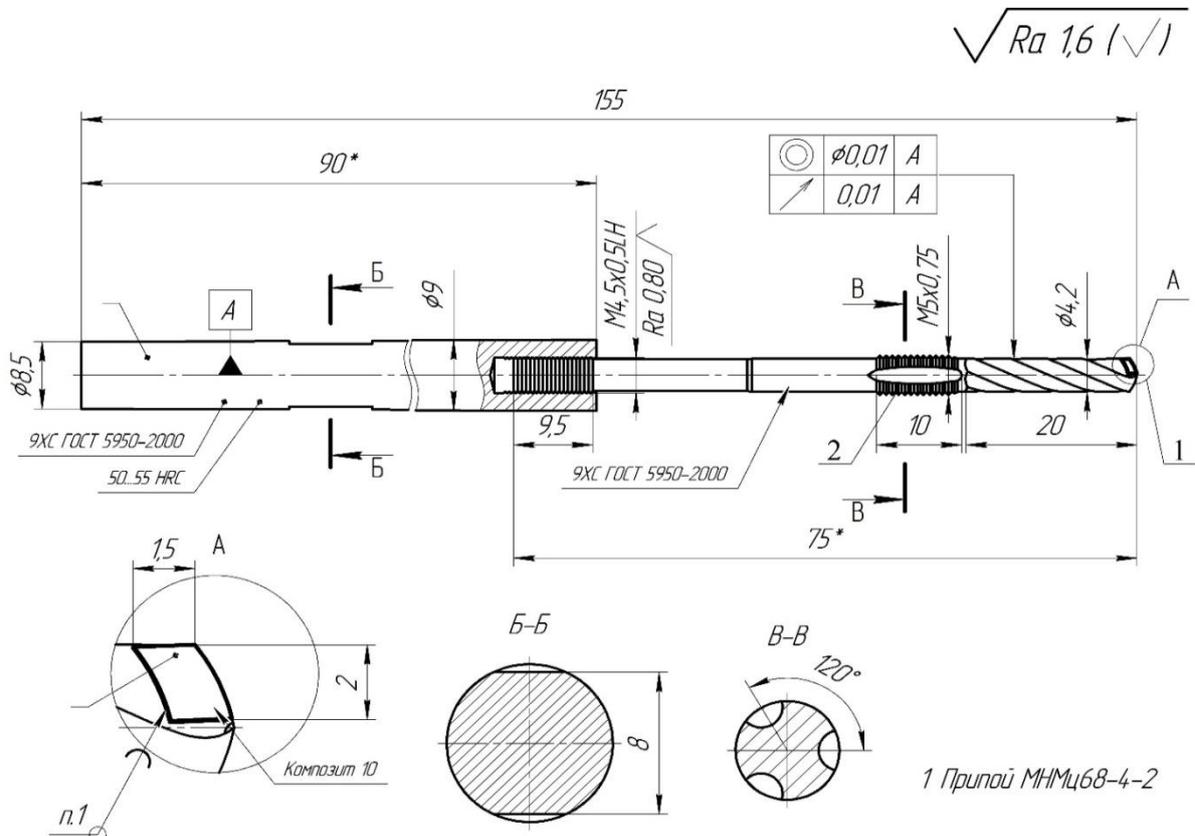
Конструкция инструмента для обработки глубоких отверстий
